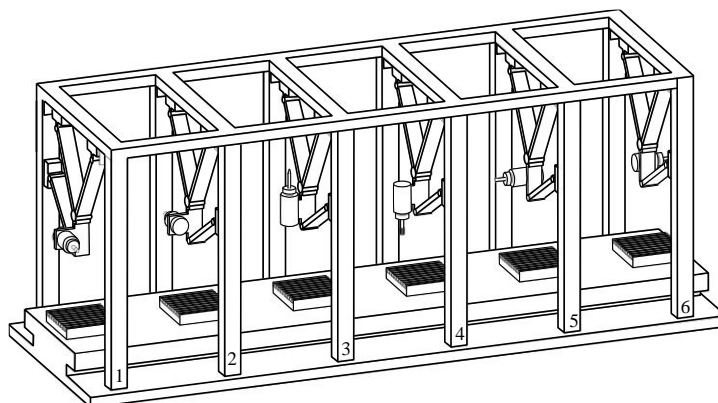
Integrated layout of the mill-drilling machine with different initial spindle orientation / Об'єднана компоновка свердильно-фрезерного верстату з різною початковою орієнтацією шпинделя
